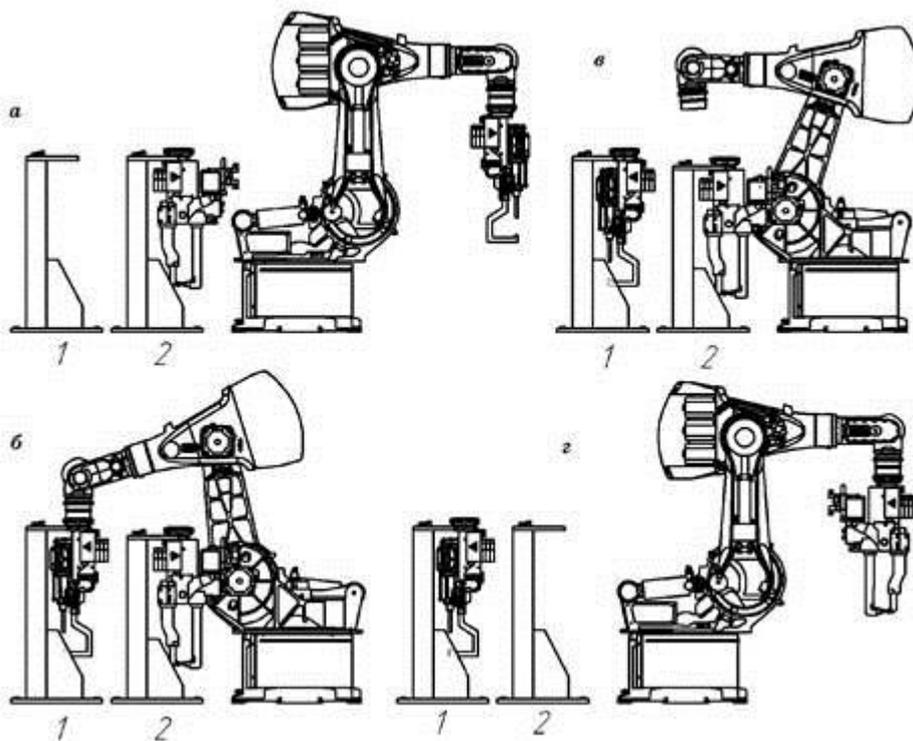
Работа устройства автоматической смены инструмента ПР для контактной сварки
